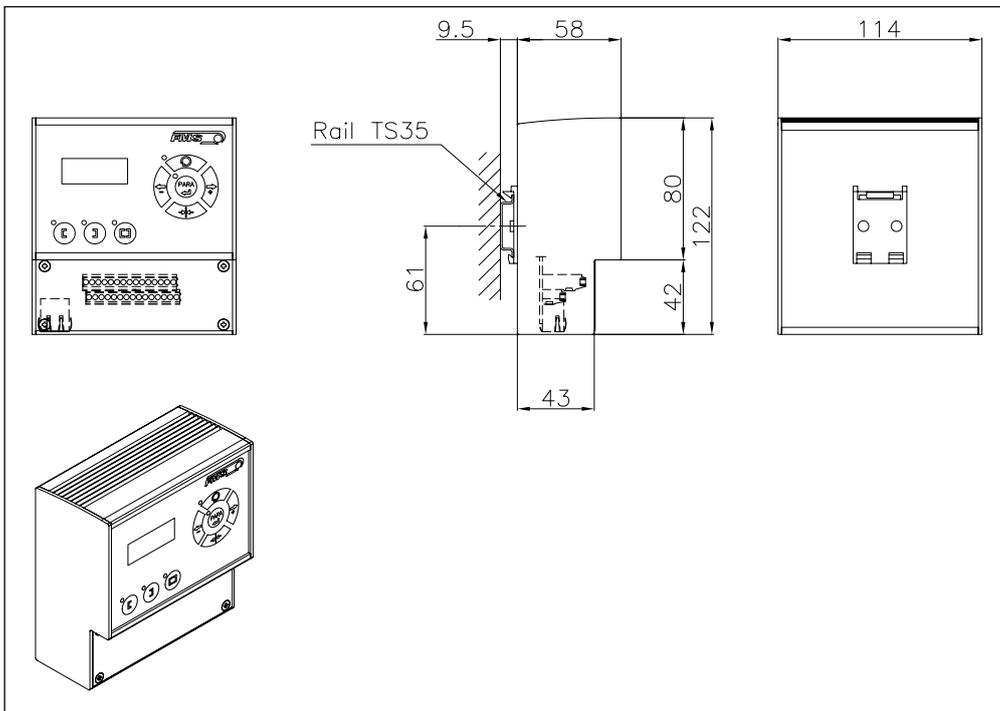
Mechanische Abmessungen BKS309.R für DIN-Schienenmontage K309006e
